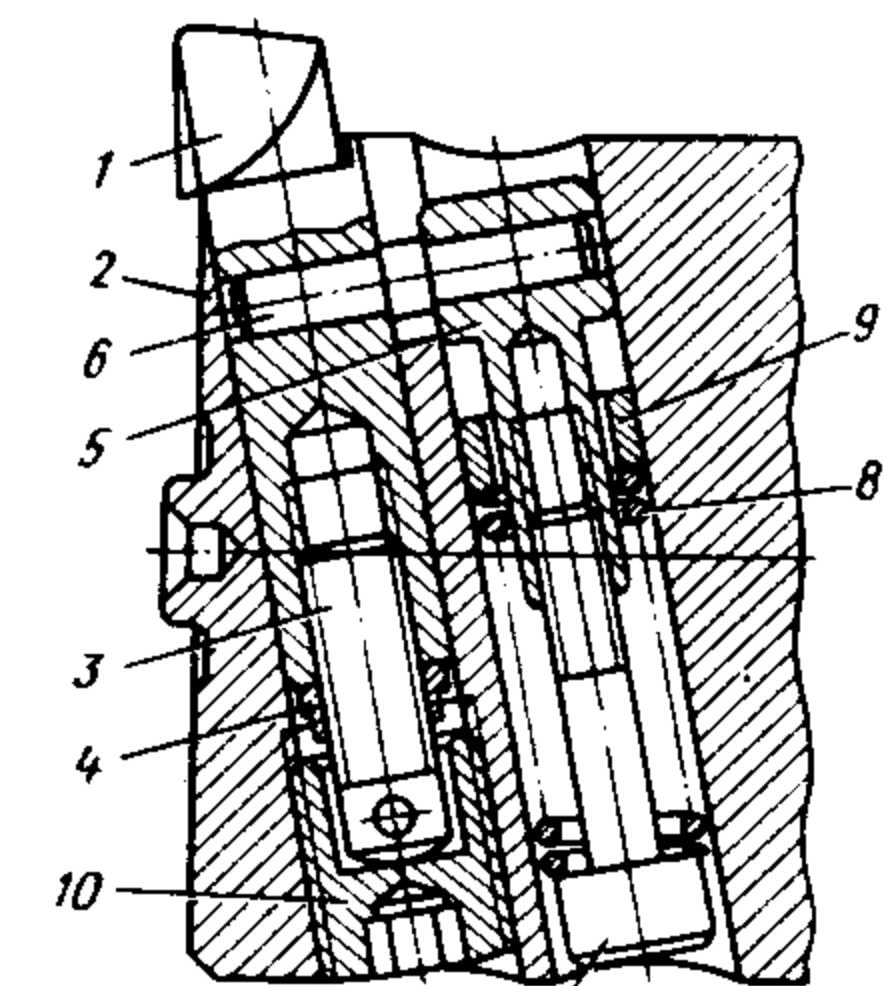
Резцовая быстросменная регулируемая вставка с резцом, установленным на размер вне борштанги
